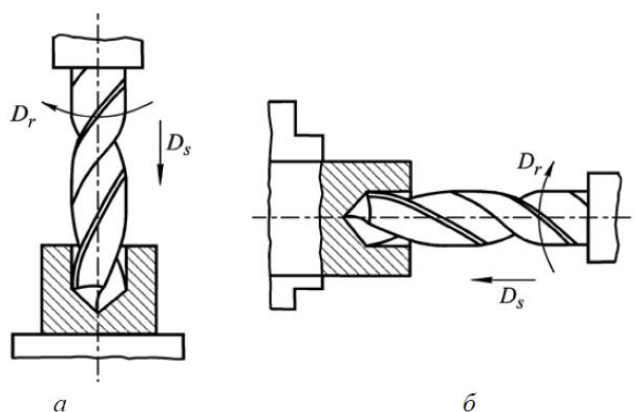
Схемы обработки отверстий на сверлильных (а) и токарных (б) станках
